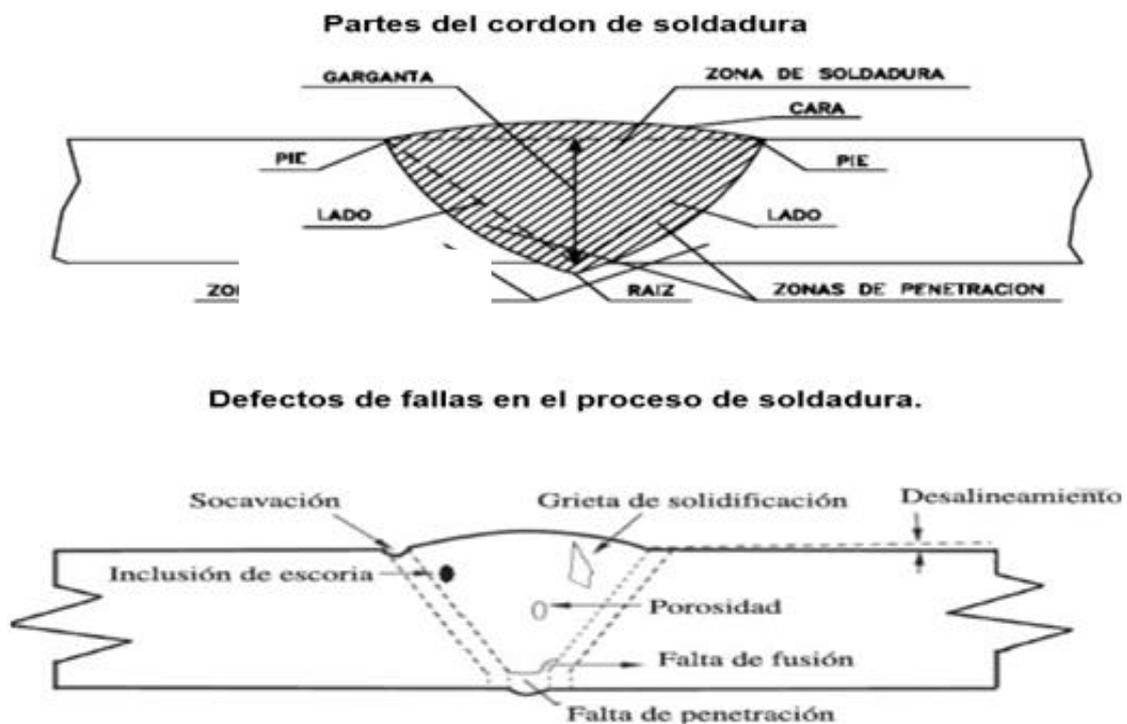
Partes y defectos del cordón de soldadura
